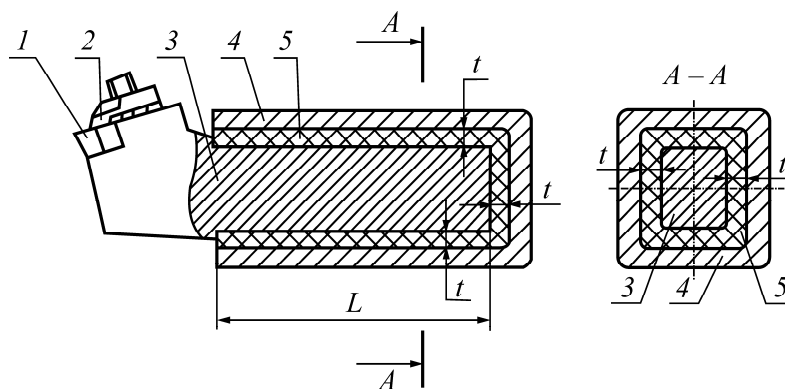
Демпфирующий резец: 1 — режущий элемент; 2 — механический прижим; 3 — державка резца; 4 — металлический стакан; 5 — демпфирующий материал
